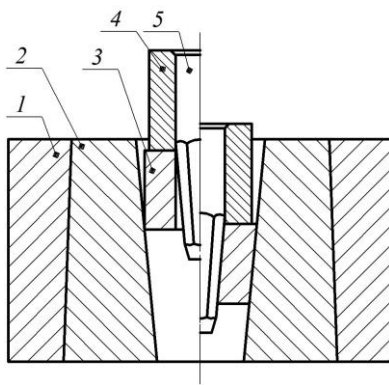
Схема видавлювання радіальним обтисненням в матриці з конічним отвором: 1 – бандаж матриці; 2 – матриця; 3 – заготовка; 4 – штовхач; 5 – майстер-пуансон
